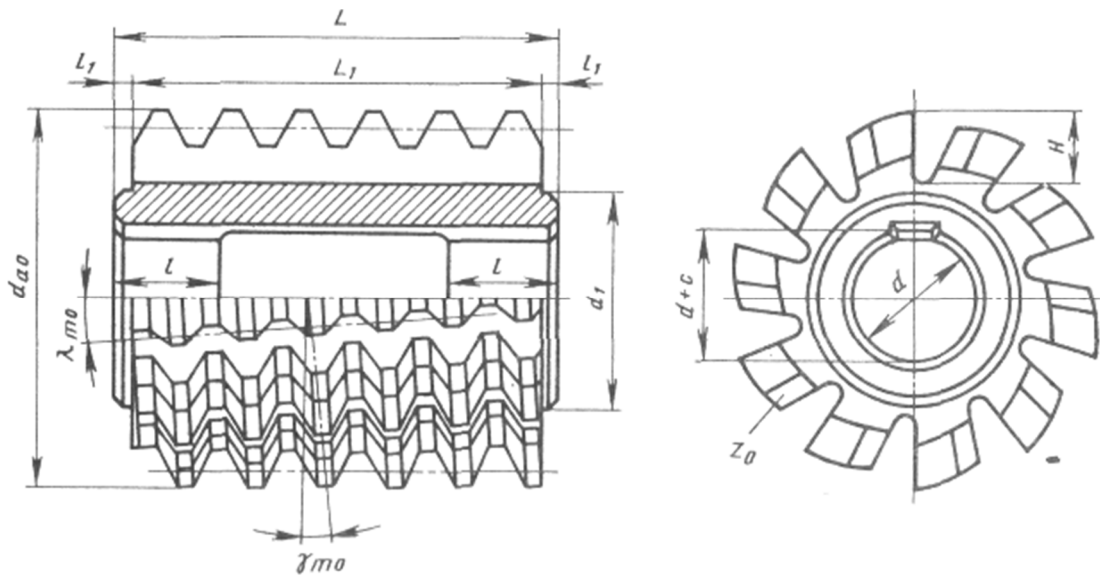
Черв'ячна зуборізна фреза, загальний вигляд.
